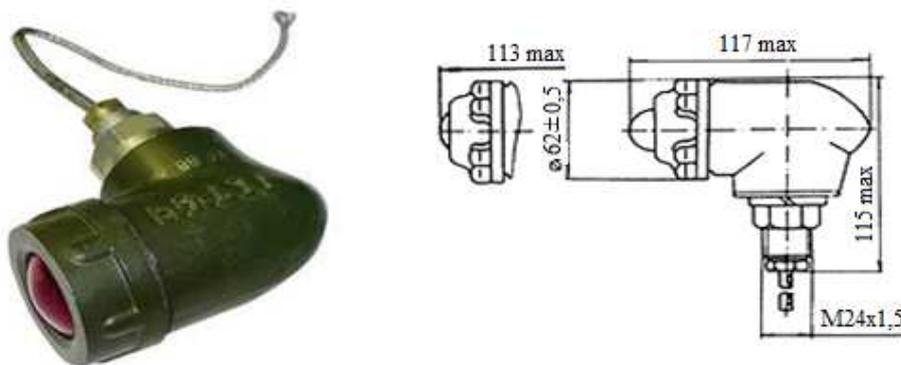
Светильник ГСТ-64-ЖЛ, внешний вид и габаритные размеры
